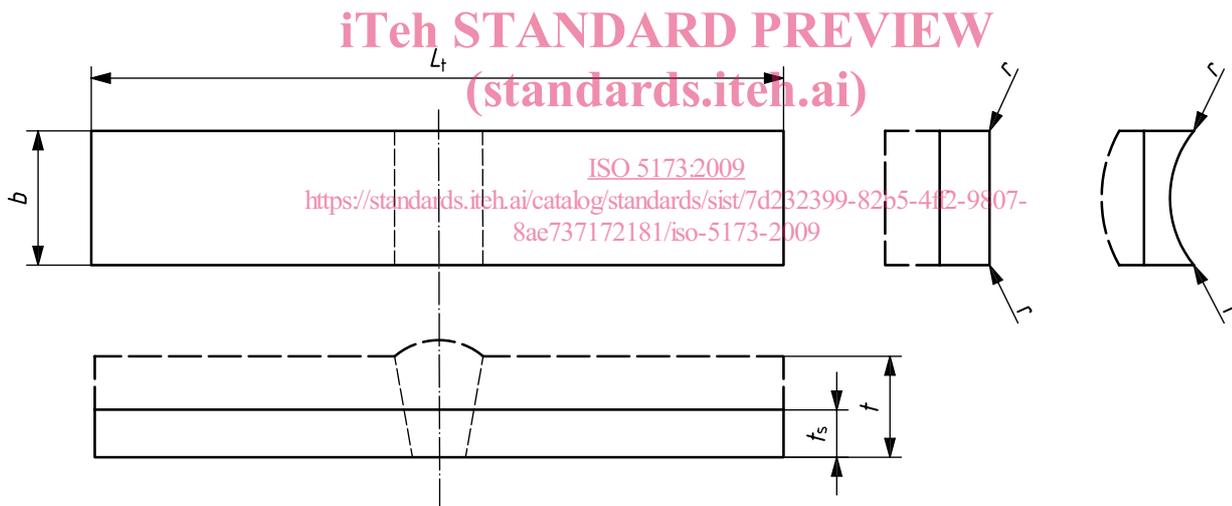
Éprouvette de pliage transversal envers sur soudure bout à bout (TRBB)
